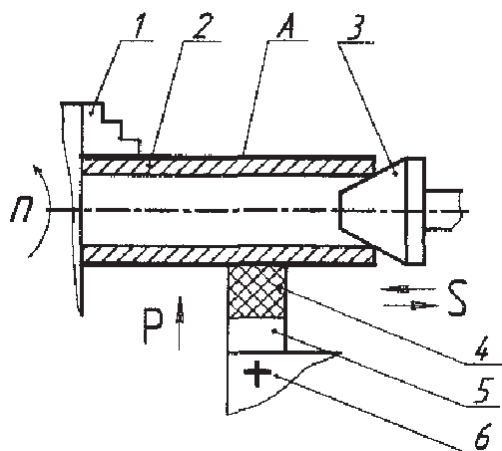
Схема нанесения защитного покрытия из жидкой среды: 1 – трехкулачковый патрон, 2 – обрабатываемая деталь, 3 – центр задней бабки, 4 – эластичный инструмент, 5 – державка инструмента, 6 – резцедержатель токарного станка, А – обрабатываемая поверхность
